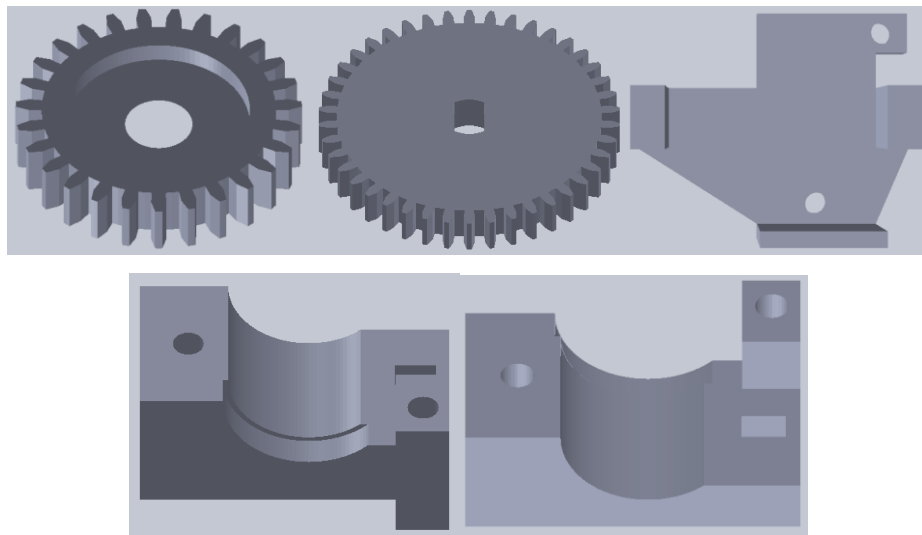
Piezas mecanismo mecánico servo válvula SolidWorks
